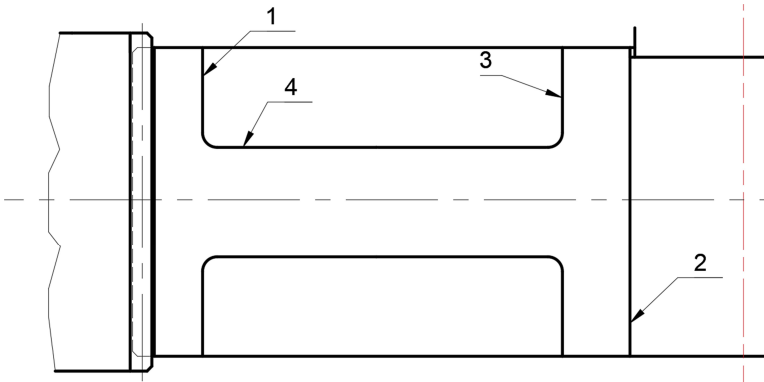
Конструкция цилиндрического зубчатого колеса
